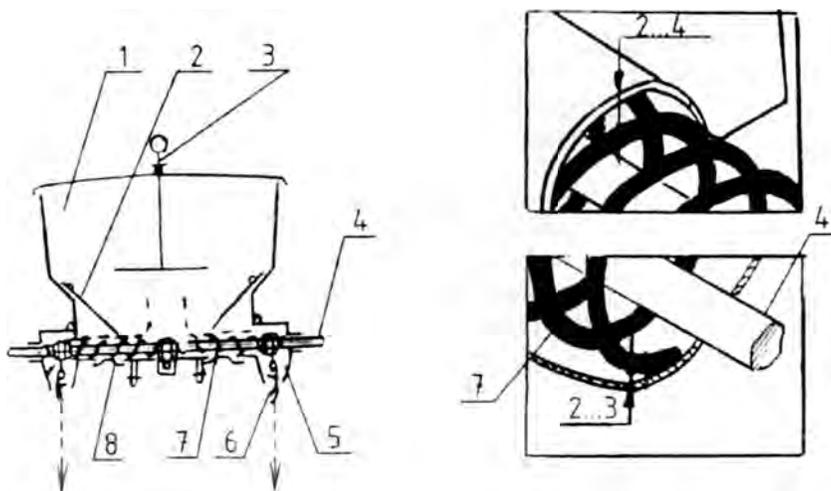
Схема туковывсевающего аппарата АТП-2:
